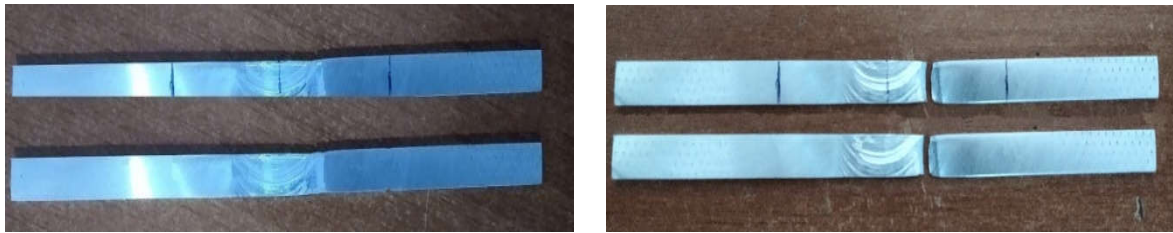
éprouvette de traction de la soudure FSW 2024.
